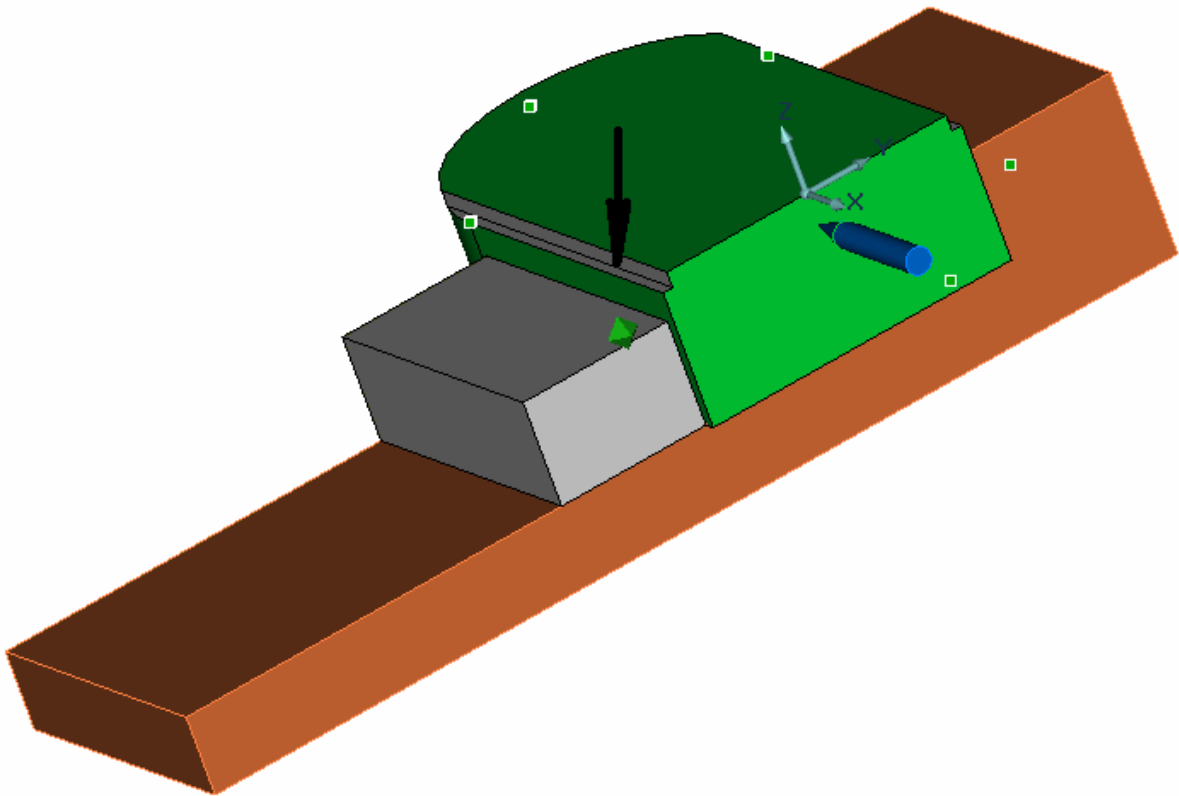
Переход на предварительной фрезерной операции 005: выполнение уступов
